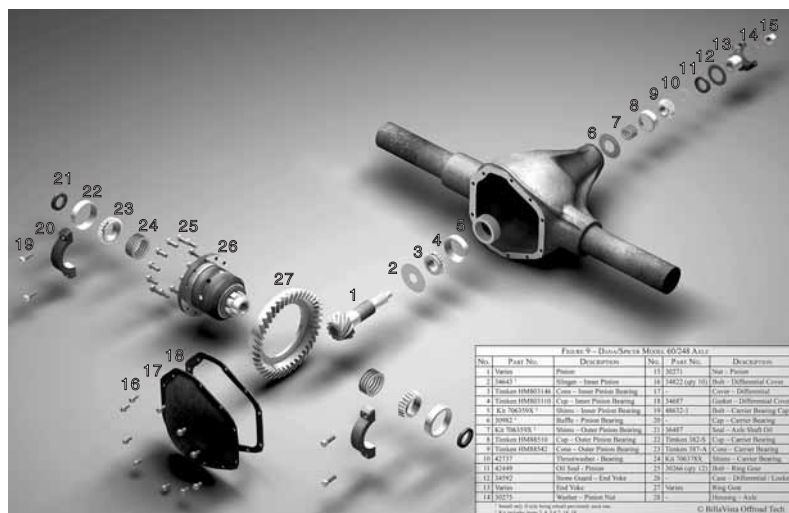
Ось Dana/Spicer модели 60/248. Список деталей: 1) шестерня; 2) маслоотражатель – внутренняя шестерня; 3) конус – внутренний подшипник ведущей шестерни; 4) крышка – внутренний подшипник ведущей шестерни; 5) прокладки – внутренний подшипник ведущей шестерни; 6) дефлектор – подшипник ведущей шестерни; 7) прокладки – внешний подшипник ведущей шестерни; 8) крышка – внешний подшипник ведущей шестерни; 9) конус – внешний подшипник ведущей шестерни; 10) упорный подшипник – подшипник; 11) сальник – шестерни; 12) решетка, защищающая от ударов камней, – концевой хомут; 13) концевой хомут; 14) кольцевая прокладка – гайка ведущей шестерни; 15) гайка – ведущая шестерня; 16) болт – крышка дифференциала; 17) крышка – дифференциал; 18) прокладка – крышка дифференциала; 19) болт – крышка опорного подшипника; 20) накладка – опорный подшипник; 21) уплотнение – смазка вала колеса; 22) крышка – опорный подшипник; 23) конус – опорный подшипник; 24) прокладки – опорный подшипник; 25) болт – кольцевое зубчатое колесо; 26) корпус – дифференциал/фиксатор; 27) кольцевое зубчатое колесо; 28) корпус – ось.
